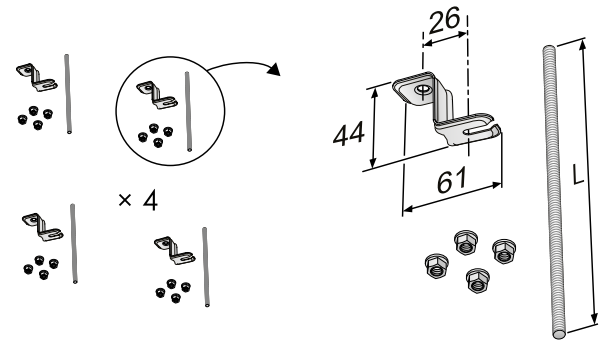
Montageteil SYST MS M8-1, Deckenbefestigung und Gewindestange
